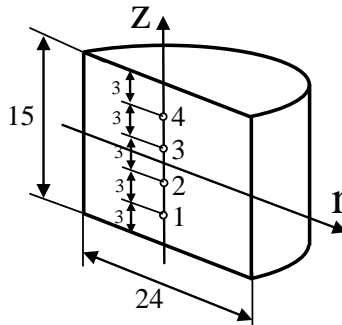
Меридіональний переріз заготовки і розташування точок 1-4 по меридіональному перерізу
